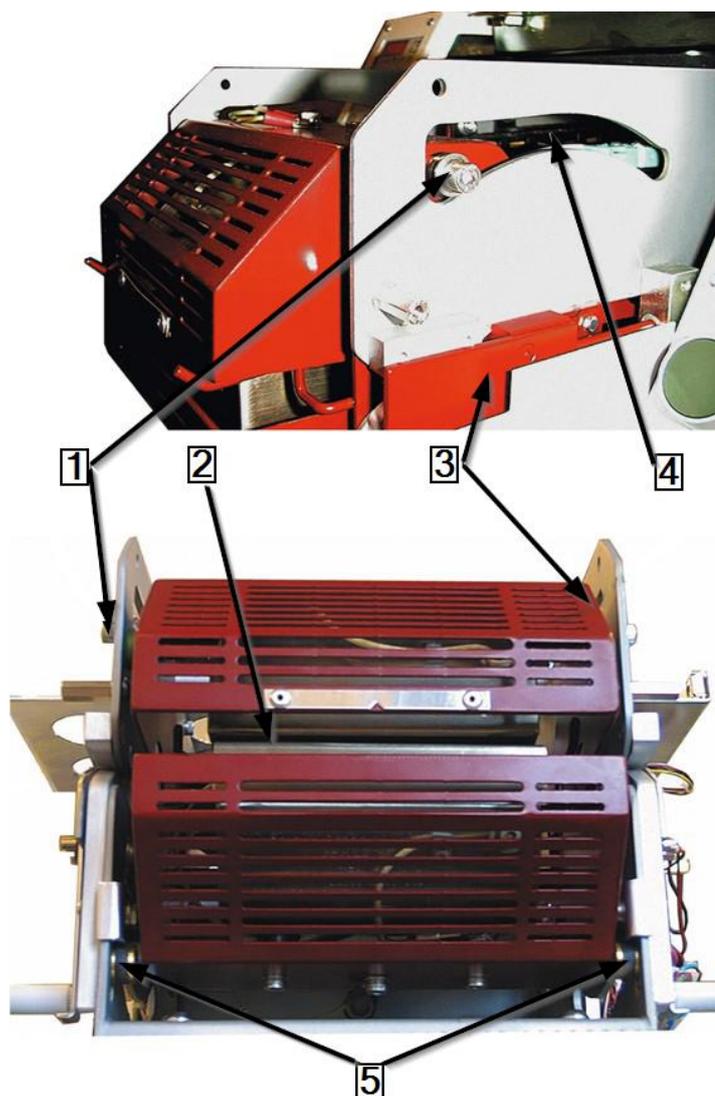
Ajuste del conjunto del carro del calentador (vista en posición avanzada)
